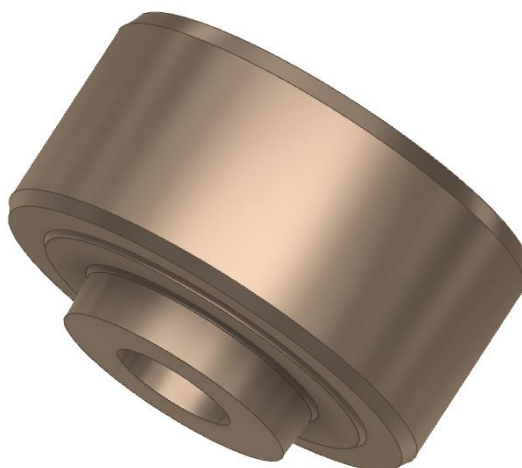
3D-заготовка корпусу розвертки
